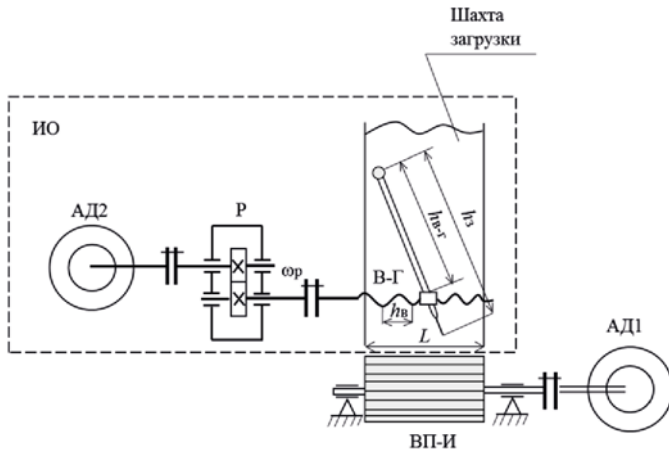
Кинематическая схема системы автоматической стабилизации загрузки вальцовой плющилки-измельчителя зерна: ВП-И – вальцовая плющилка-измельчитель; ИО – исполнительный орган (асинхронный двигатель АД2 + редуктор Р + винт-гайка В-Г); АД1 – приводной асинхронный двигатель вальцов; L – длина вальца, м; $h_в$ – шаг резьбы В-Г, м/виток; $h_з$ – расстояние от оси поворота заслонки до ее края, м; $h_{в-г}$ – среднее расстояние от оси поворота заслонки до гайки В-Г, м
